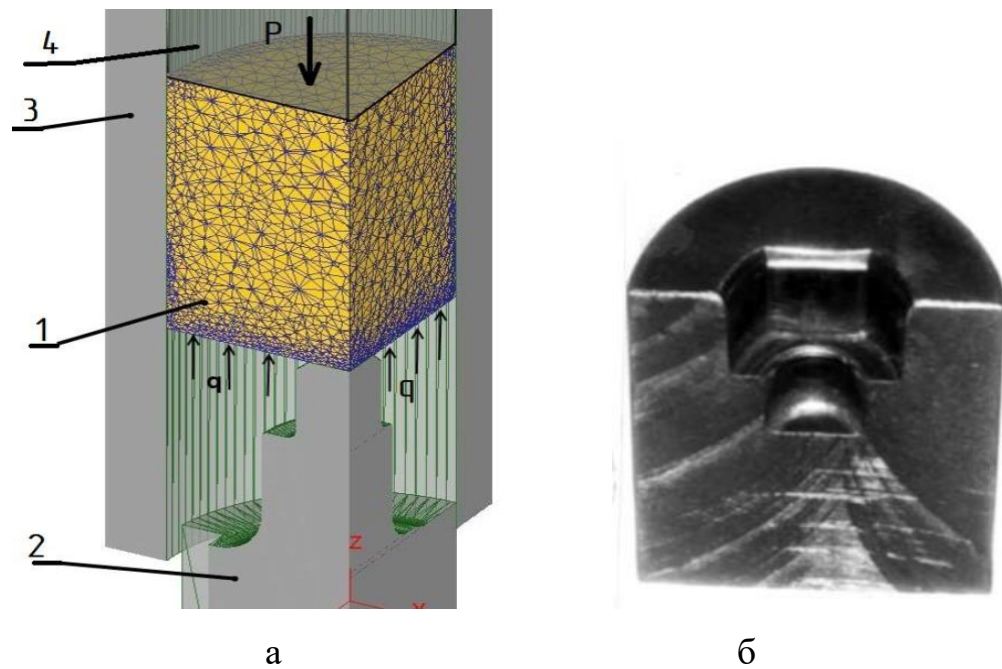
Схема видавлювання (а) ступінчатої порожнини зі сталі 12ХН3А та заготовки (б) [105, 106]
